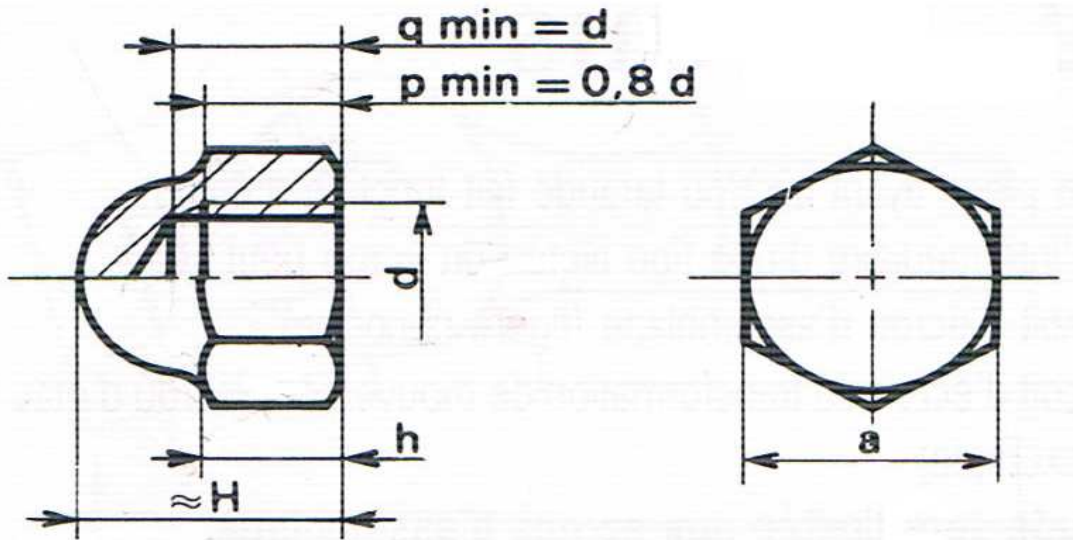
4 : Profil des dimensions d'un écrou borgne
